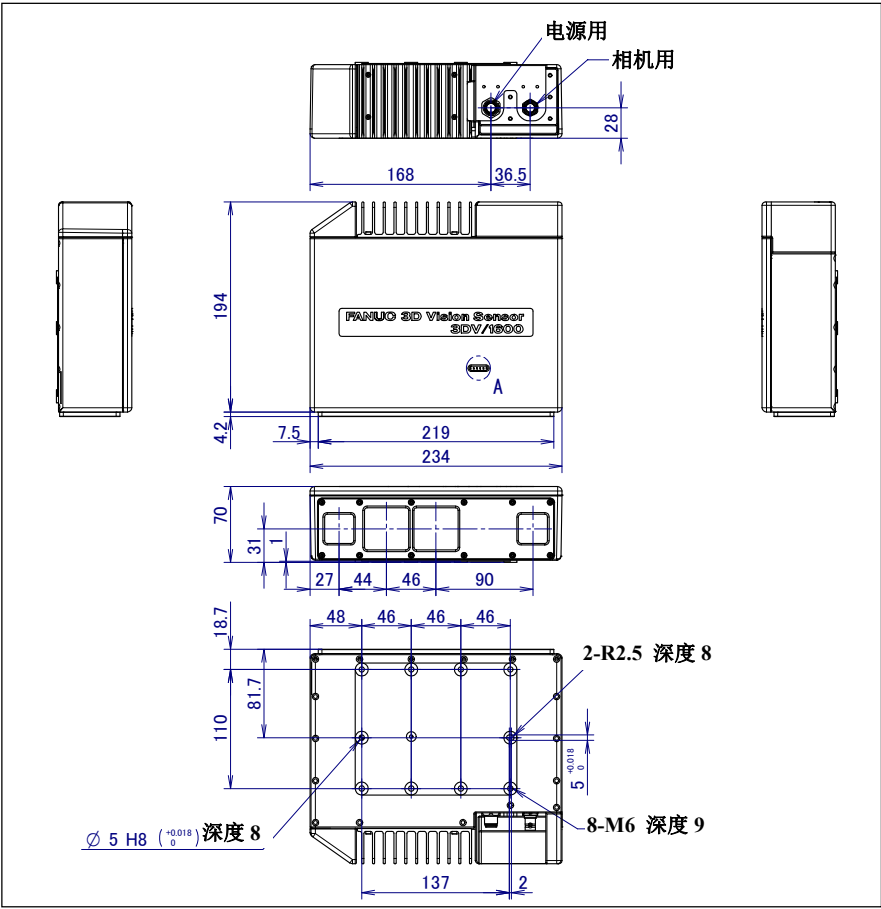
(c) 3D 视觉传感器外形尺寸 (3DA/1600, 带有 LED)
